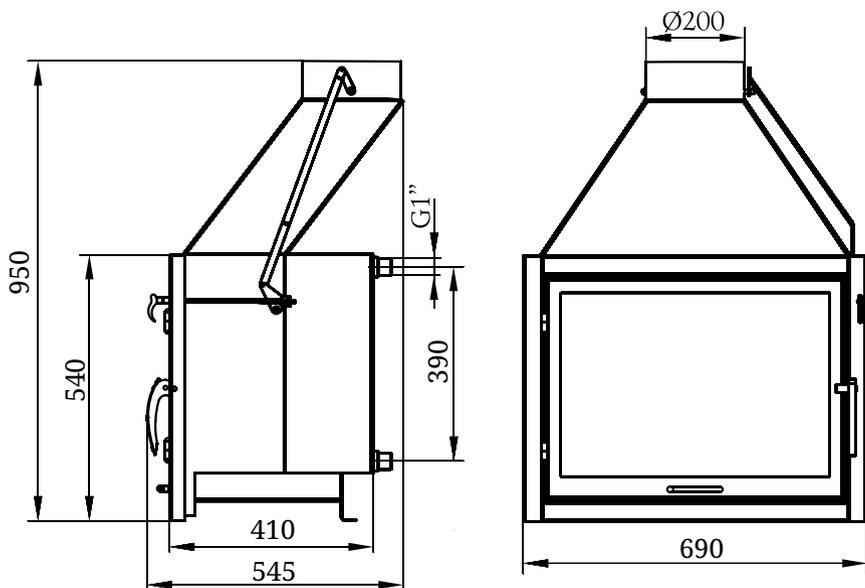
Габаритные размеры каминной топки «Аквариус ТО»
